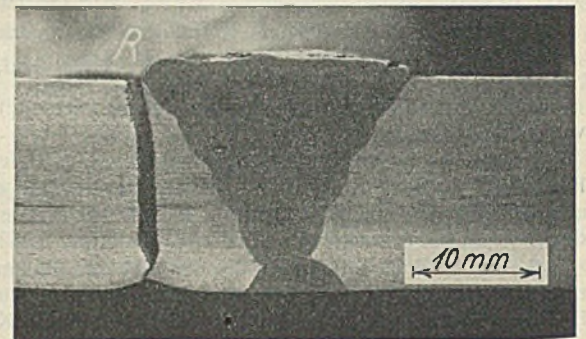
Querschnitt durch eine V-Naht. (Lichtbogenschweißung, Gleichstrom, blanke Elektroden) nach oftmals wiederholter Zugbelastung. Beginn des Dauerbruchs bei *R* infolge plötzlicher Querschnittsänderung.
